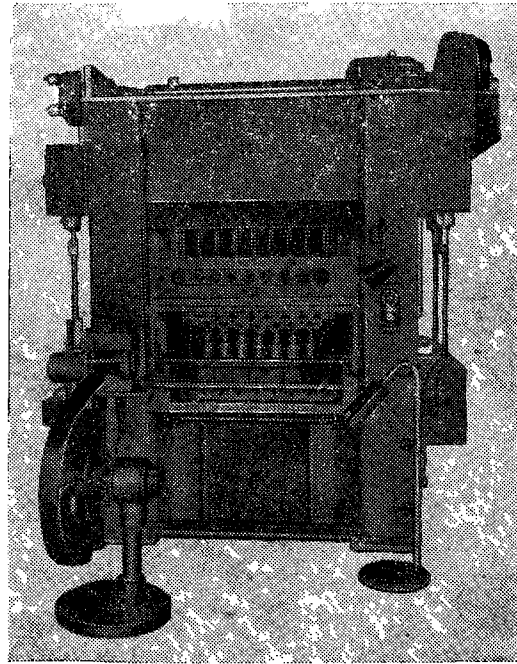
Многопозиционный кривошипный пресс-автомат с закрытым приводом А6124 для листовой штамповки
